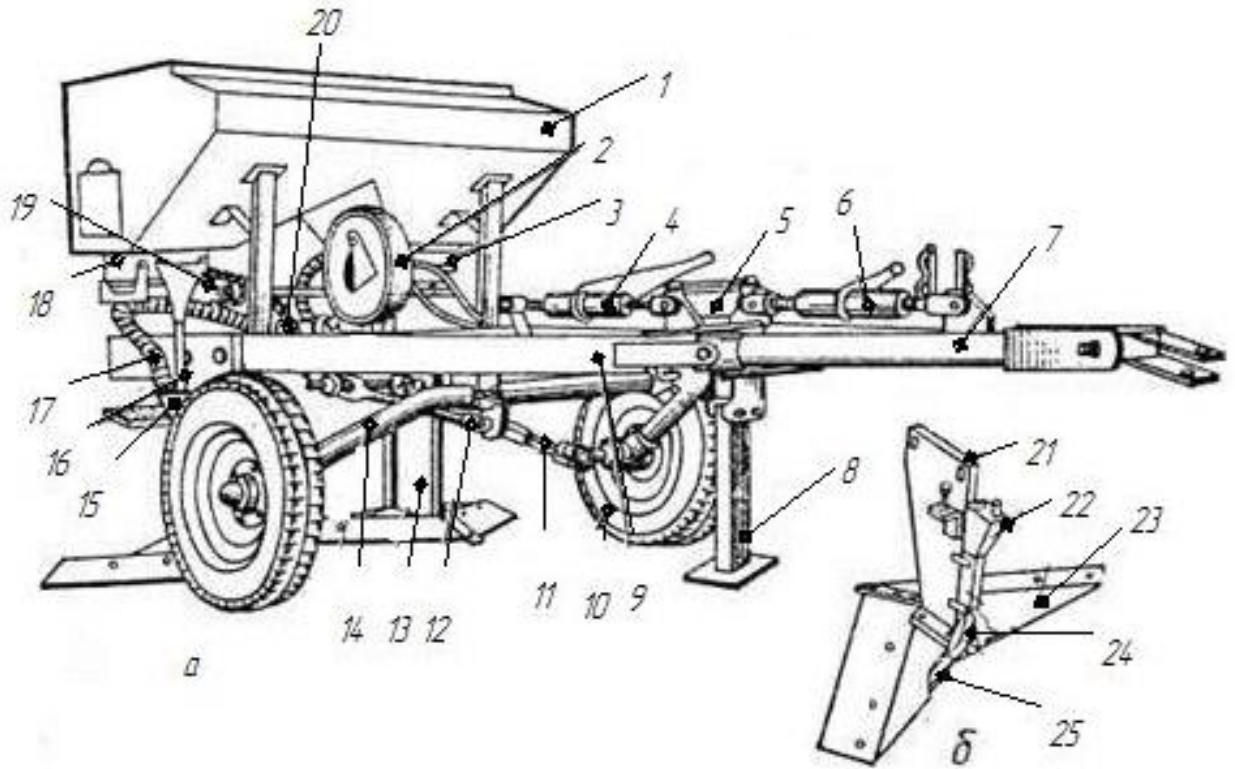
Культиватор КПГ-2,2 плоскорез-глубококорыхлитель с приспособлением для внесения удобрений: *а* – общий вид; *б* – рабочий орган; 1 – бункер для минеральных удобрений; 2 – вентилятор; 3 и 18 – дозаторы; 4 – винтовая стяжка механизма регулирования глубины; 5 – гидроцилиндр механизма подъема; 6 – винтовая стяжка прицепа; 7 – удлинитель; 8 – подставка; 9 – рама; 10 – опорные колеса; 11 – карданная передача; 12 – вилка выключения привода дозаторов; 13 – рабочий орган; 14 – коленчатая ось; 15 – туконаправитель; 16 – тукопровод; 17 – воздухопровод; 19 – приводной вал; 20 – цепь привода дозаторов; 21 – стойка; 22 – смесительная камера; 23 – башмак; 24 – делитель; 25 – канал
